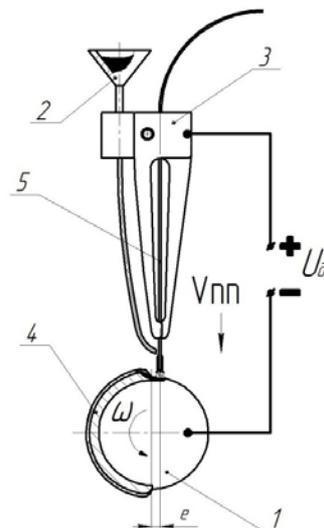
Схема процесса электродуговой наплавки с ферромагнитной шихтой: 1 – деталь; 2 – бункер с шихтой; 3 – сварочная головка; 4 – наплавленный металл; 5 – сварочная проволока.
